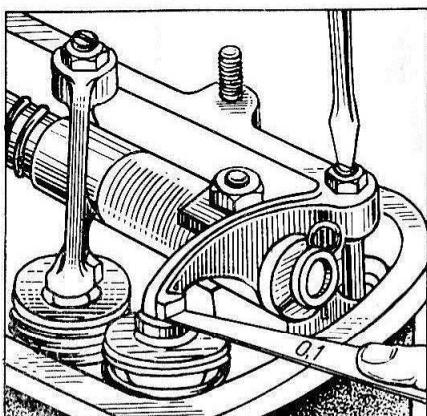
Регулировка зазора между коромыслом и клапаном.
